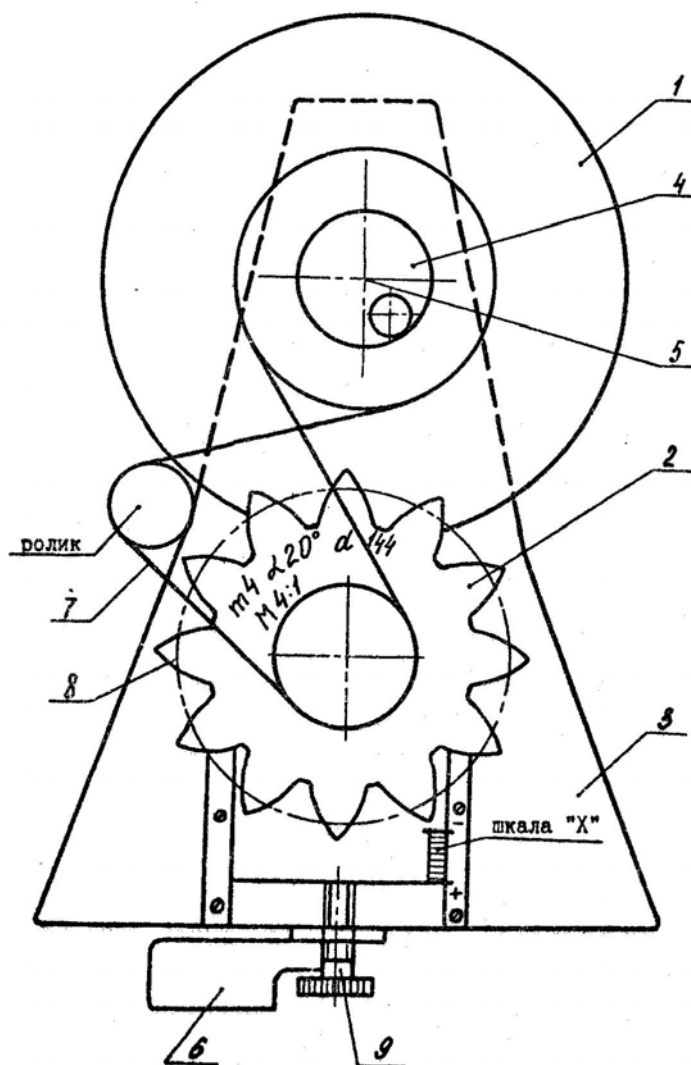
Схема прибора для построения эвольвентных профилей зубьев
